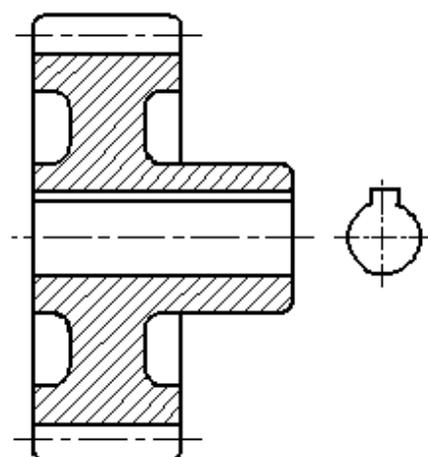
Образец изображения отверстия в ступице зубчатого колеса
